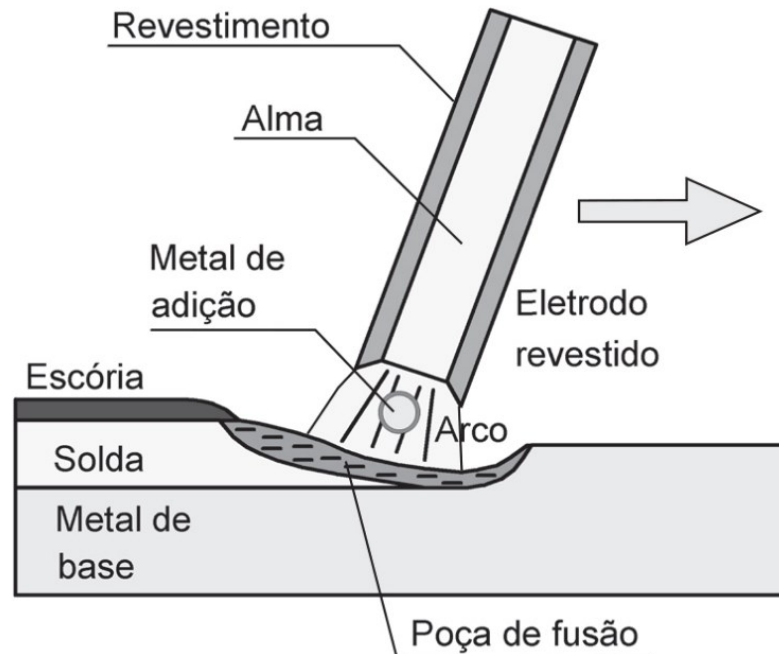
Esquema de soldagem com eletrodo revestido (MARQUES, 2016).
